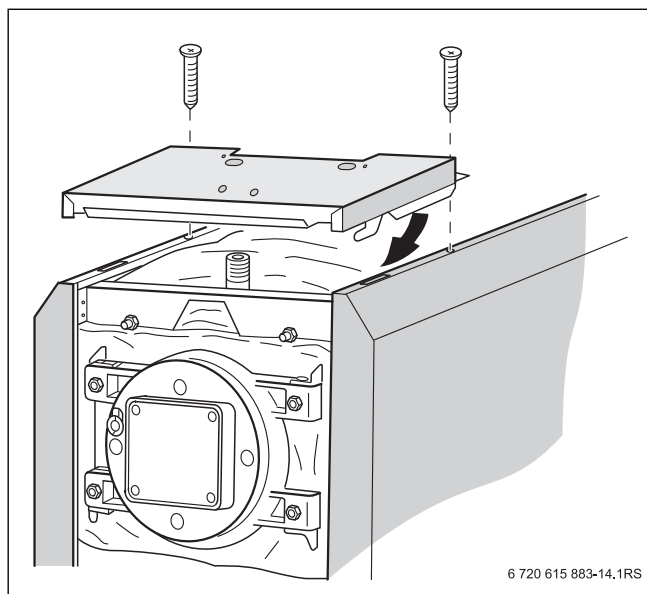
Položení dílů krytu kotle - principiální zobrazení
